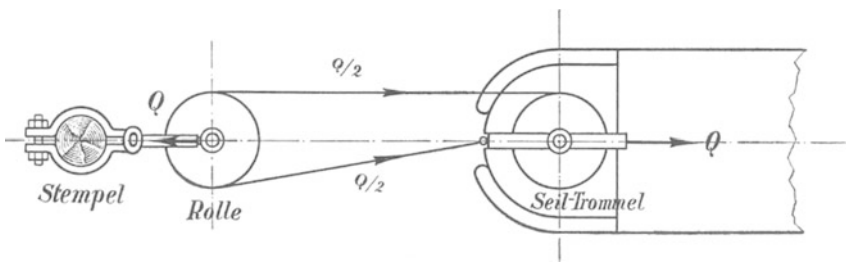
Umkehrung der losen Rolle an der Schrämmaschine.
